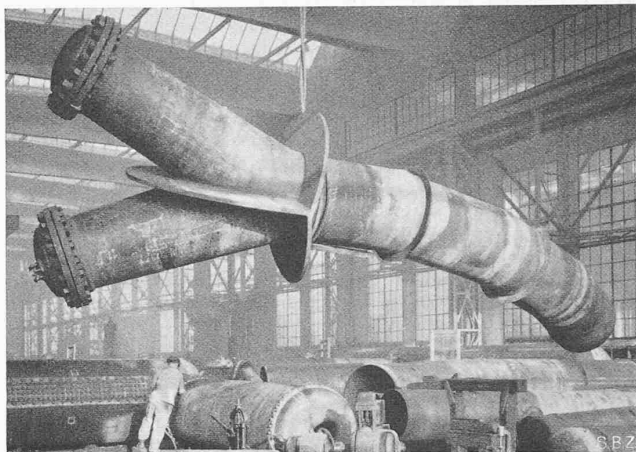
Hosenrohr einer Druckleitung mit aufgeschweisster Kragenverstärkung
